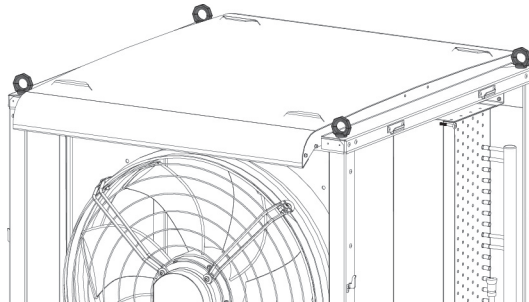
Wärmepumpe mit eingeschraubten Ringschrauben
